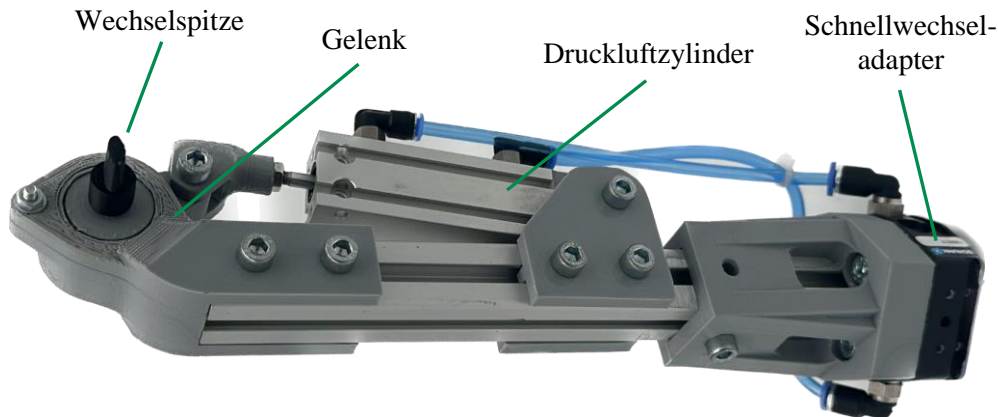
Mit ovalen Wechselspitzen ausgestattetes Demontagewerkzeug zum Aufhebeln von Gehäusedeckeln (SGripper_02)
